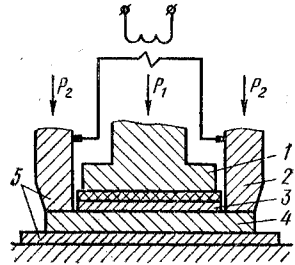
Схема сварки по способу А. М. Игнатъева
